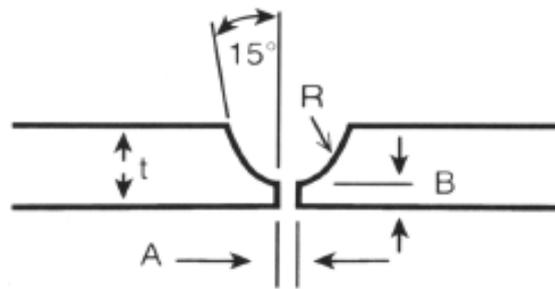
Junta para soldadura a tope de chapas
